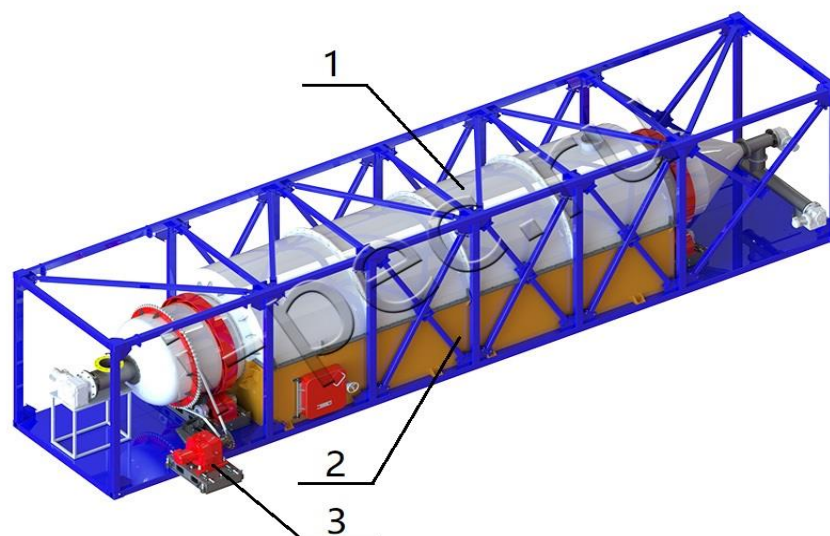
Установка термической деструкции УТД-2-1000 с вращающимся корпусом реактора:
